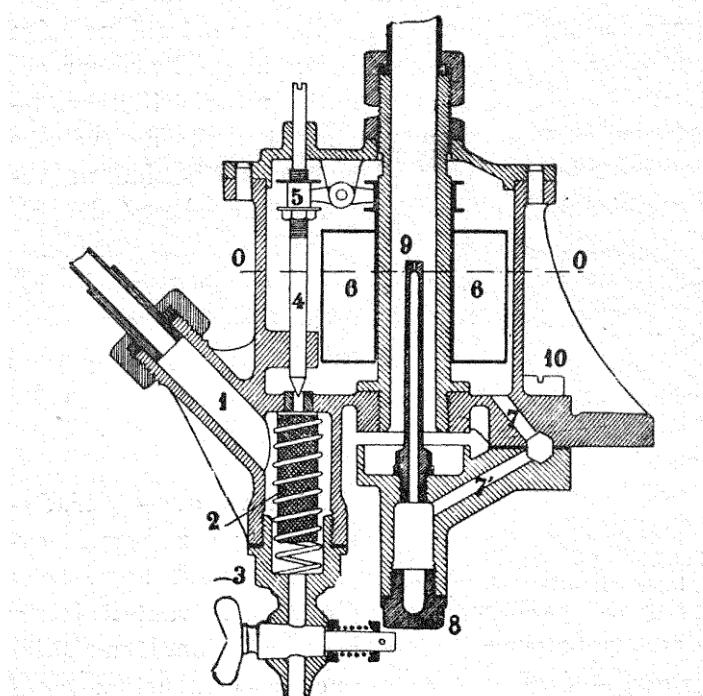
Carburateur automatique (de Dion-Bouton).
